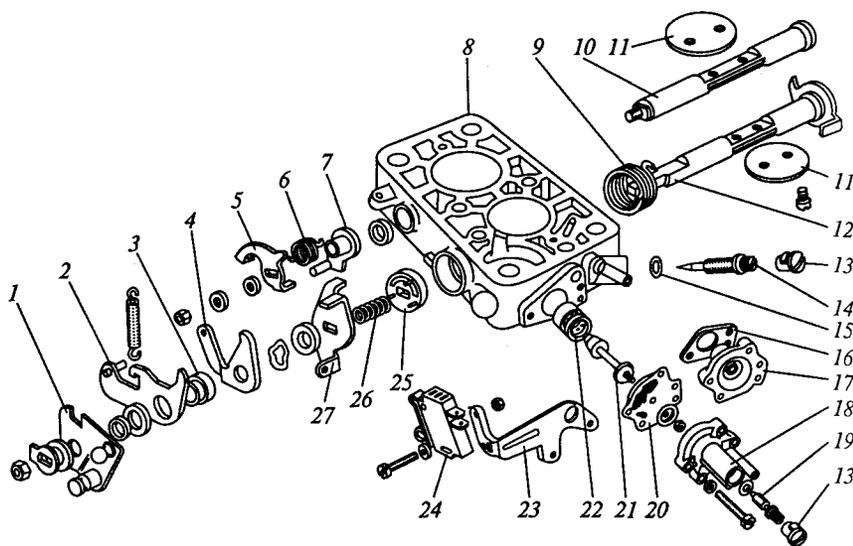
Детали корпуса дроссельных заслонок карбюратора 2105-1107010: 1 — рычаг привода дроссельных заслонок; 2 — рычаг, ограничивающий открытие дроссельной заслонки второй камеры; 3 — втулка; 4 — рычаг связи с воздушной заслонкой; 5 — рычаг, закрепленный на оси дроссельной заслонки второй камеры; 6 — пружина; 7 — рычаг, связанный с пневмоприводом; 8 — корпус дроссельных заслонок; 9 — возвратная пружина первой дроссельной заслонки; 10 — ось второй дроссельной заслонки; 11 — дроссельные заслонки; 12 — ось первой дроссельной заслонки; 13 — ограничительные втулки; 14 — винт регулировки состава смеси холостого хода; 15 — уплотнительное кольцо; 16 — прокладка экономайзера; 17 — корпус экономайзера принудительного холостого хода; 18 — крышка экономайзера; 19 — винт регулировки количества смеси холостого хода; 20 — диафрагма экономайзера; 21 — игла экономайзера; 22 — седло иглы; 23 — кронштейн крепления микропереключателя; 24 — микропереключатель; 25 — золотник; 26 — пружина золотника; 27 — рычаг, закрепленный на оси первой дроссельной заслонки
